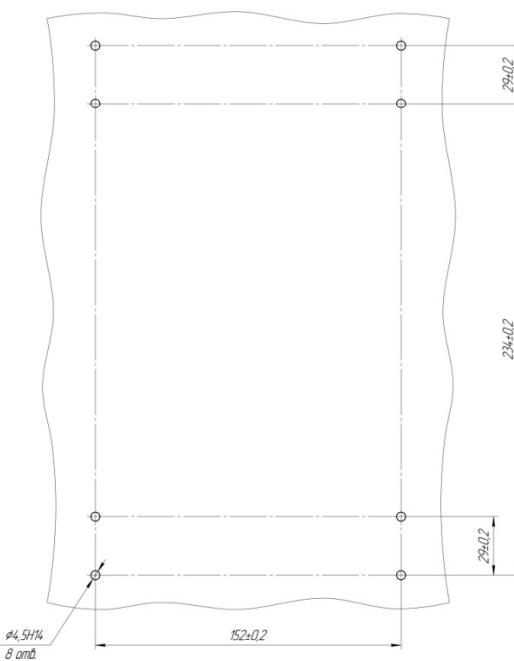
Габаритные и присоединительные размеры устройства PC830-M1 при внешнем монтаже, обеспечивающем его поворот влево/вправо
